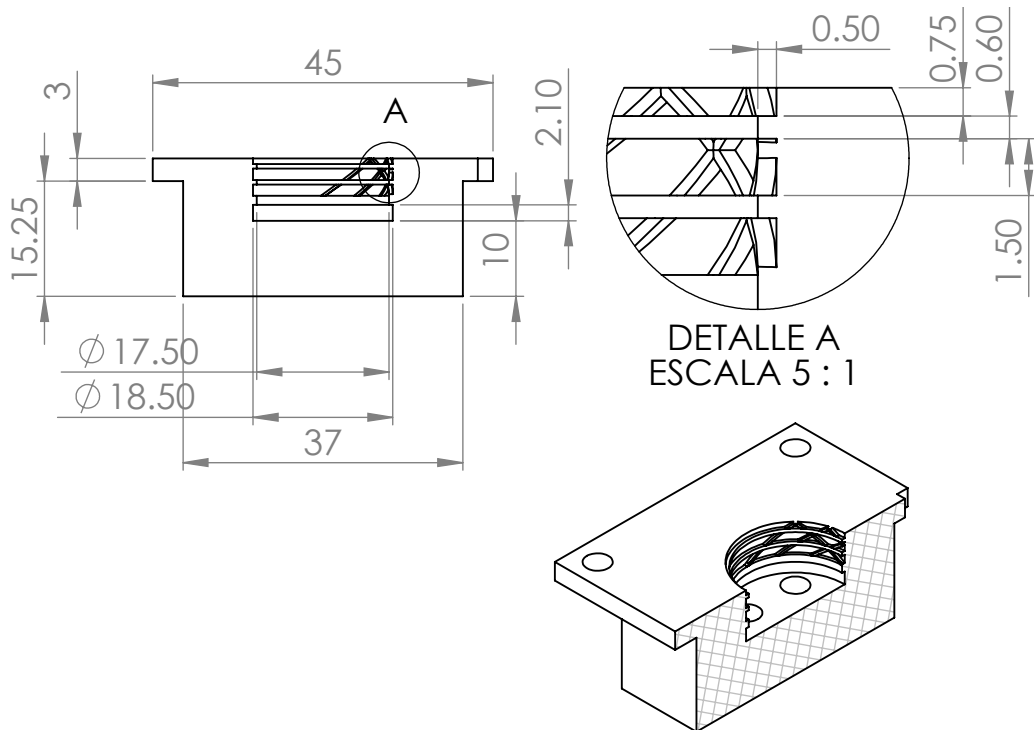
Vista en corte del molde del *Robot Tilt* parte B
